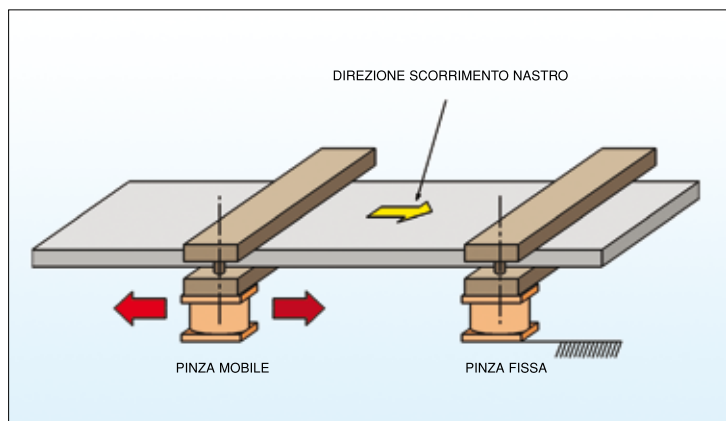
Schema alimentatore a pinze ad 1 pinza mobile
